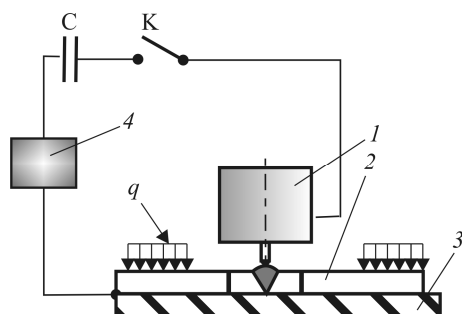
ЭДО образцов сварных соединений при “жестком” закреплении: С – емкостный накопитель энергии; К – силовой ключ; q – фиксирующая нагрузка; 1 – электродное устройство; 2 – образец; 3 – сборочная плита; 4 – датчик Холла.
